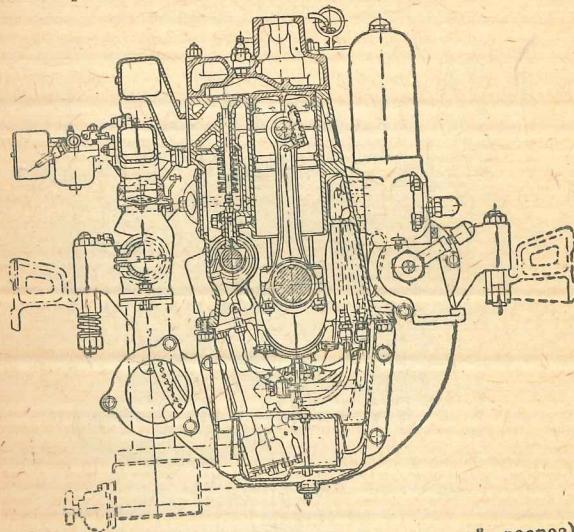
Двигатель ЗИС-21 (поперечный разрез)
